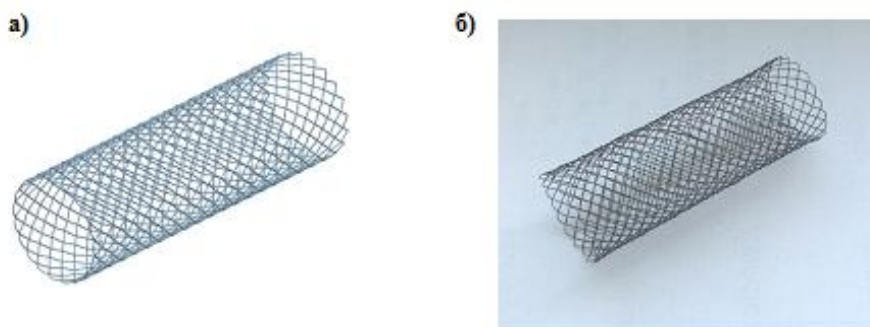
3D-модель колоректального стента (а) и изготовленный образец изделия (б)
